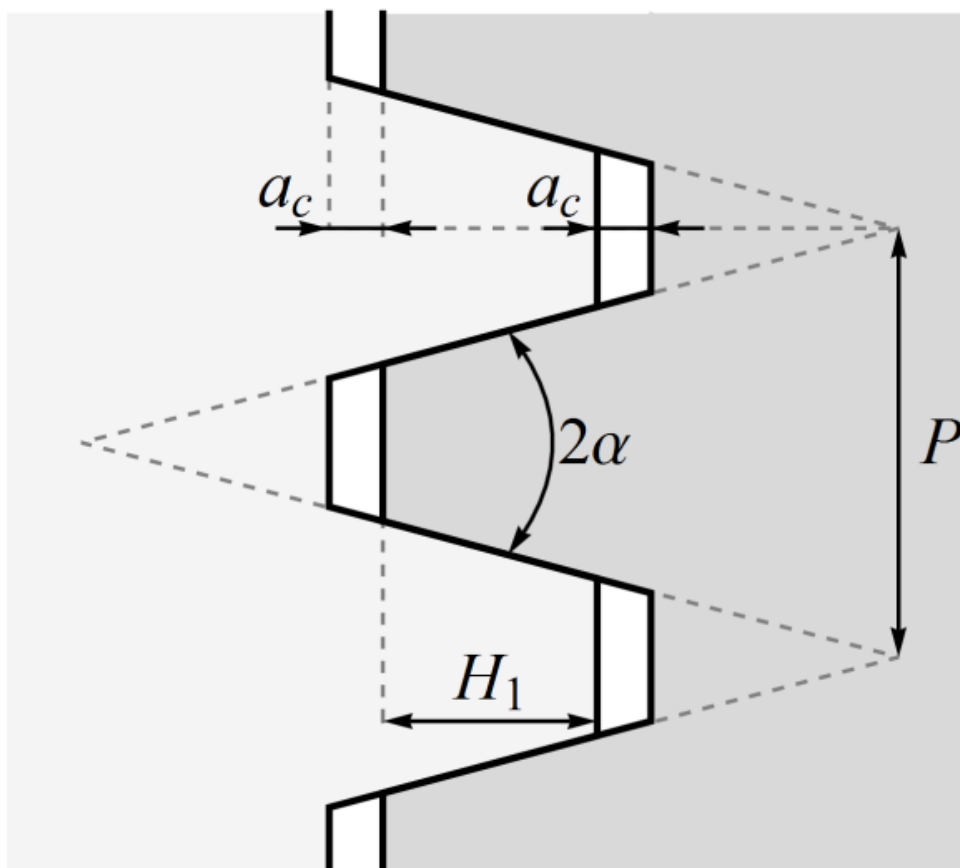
Размеры трапециевидального профиля передачи винт-гайка [13]
